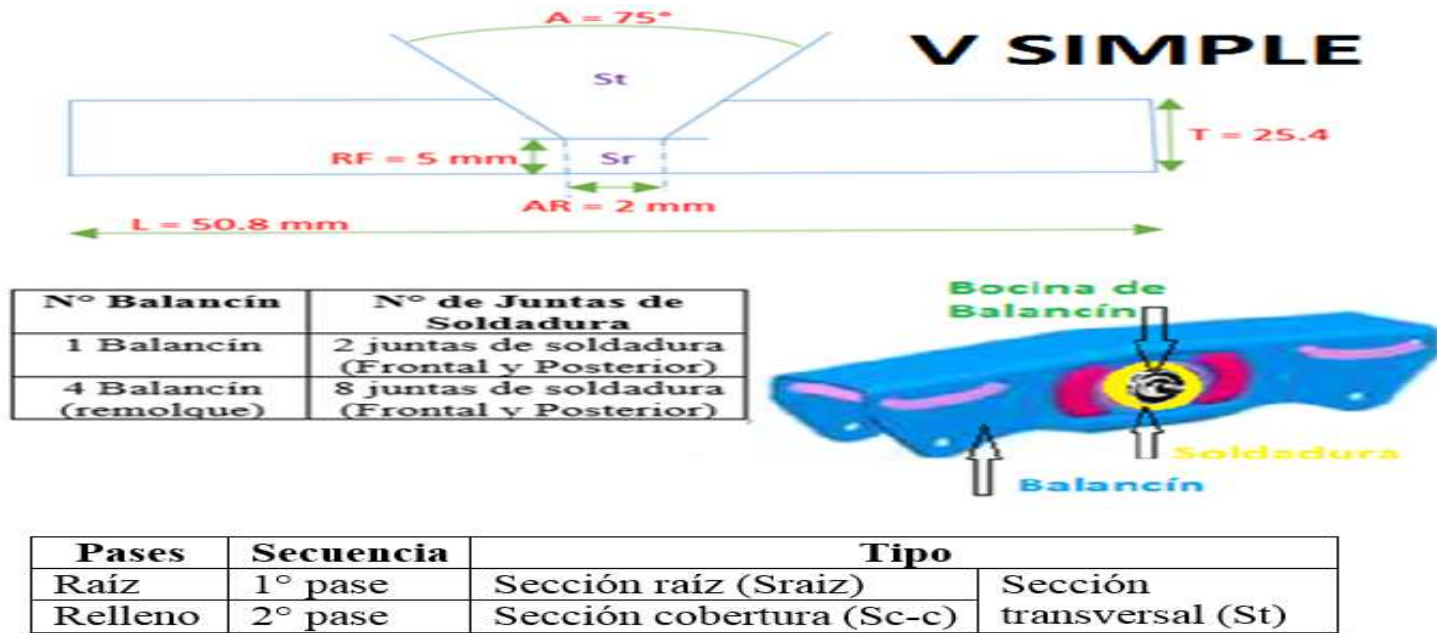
Medidas del área a soldar: Bocina - Balancín (En V Simple)
